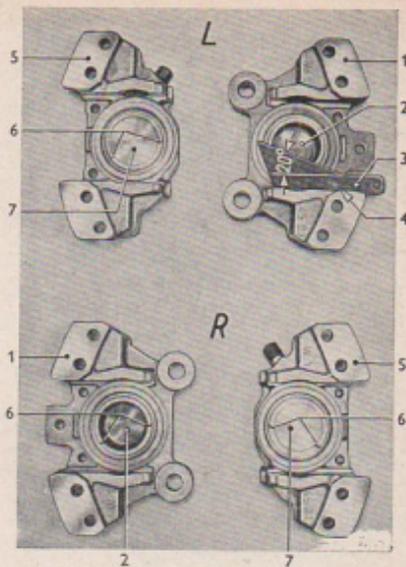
Einbaulage des Kolbens im Flansch- und Deckelgehäuse des linken und rechten Bremsatzels
